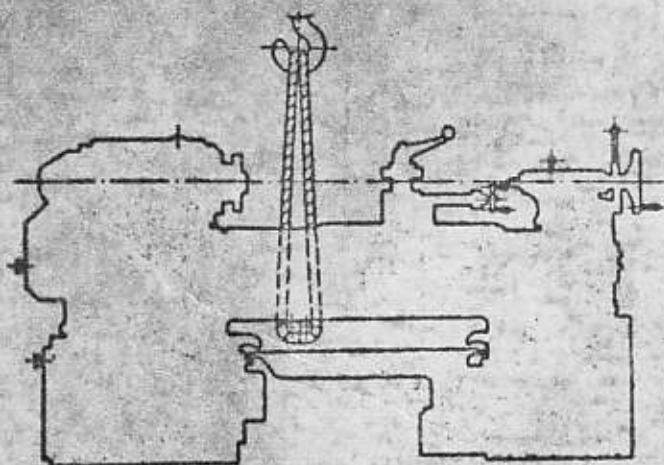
СХЕМА ТРАНСПОРТИРОВКИ
